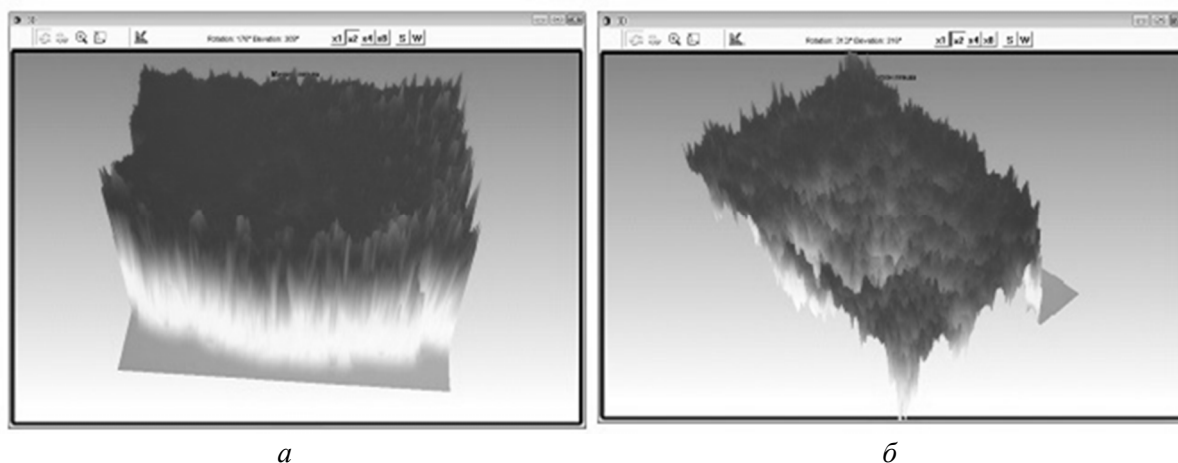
3D профиль шероховатости поверхности образцов из стали 40X: а – после обработки пластическим деформированием; б – после обработки пластическим деформированием с добавлением геомодификатора трения
